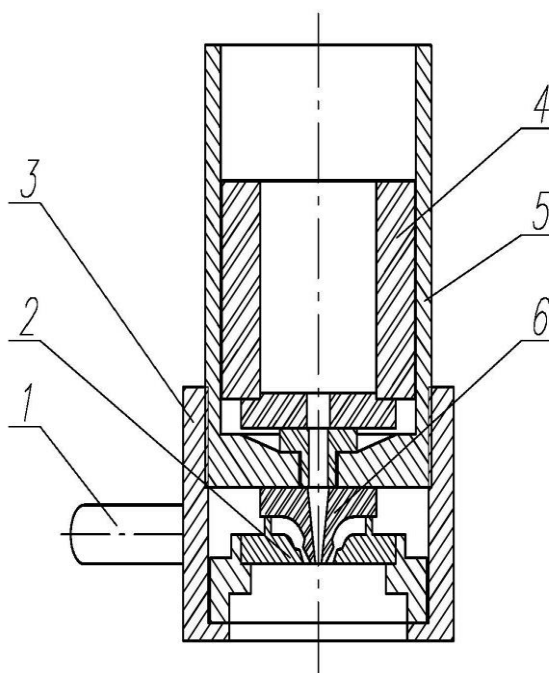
Диспергатор в разрезе: 1 – патрубок; 2 – сопло; 3 – корпус; 4 – футеровка; 5 – стакан; 6 –золотник
